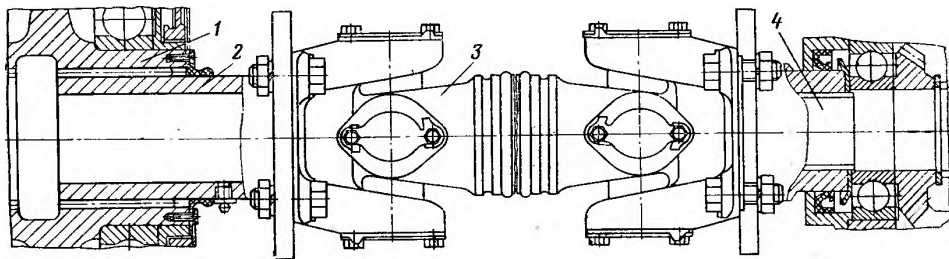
Второй карданный вал экскаватора ЭТР253
